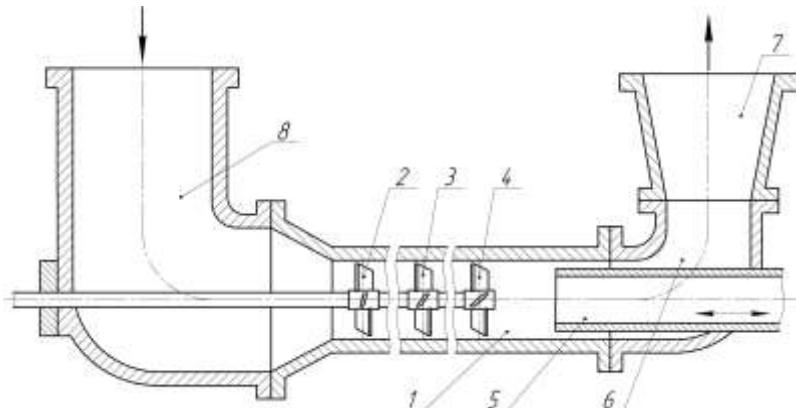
Пристрій для кавітаційної обробки сусpenзій:
